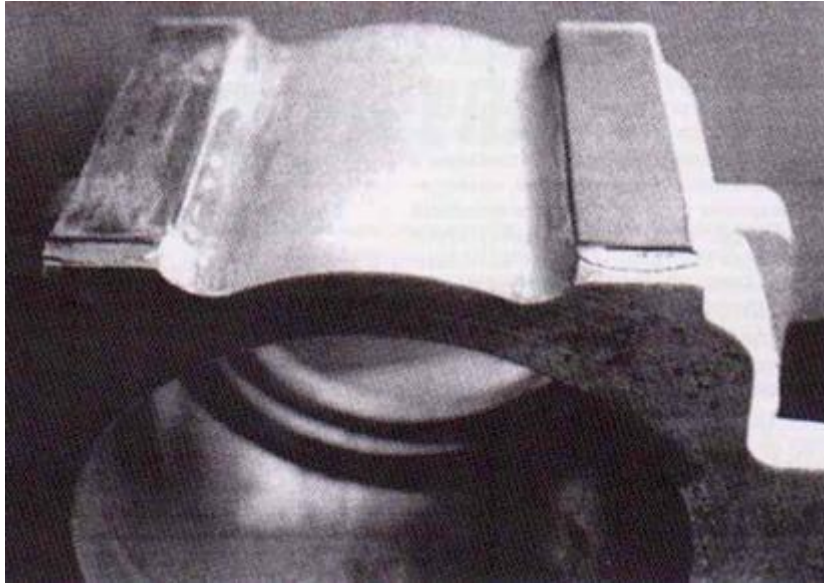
Корпус букси з привареними сталевими пластинами
